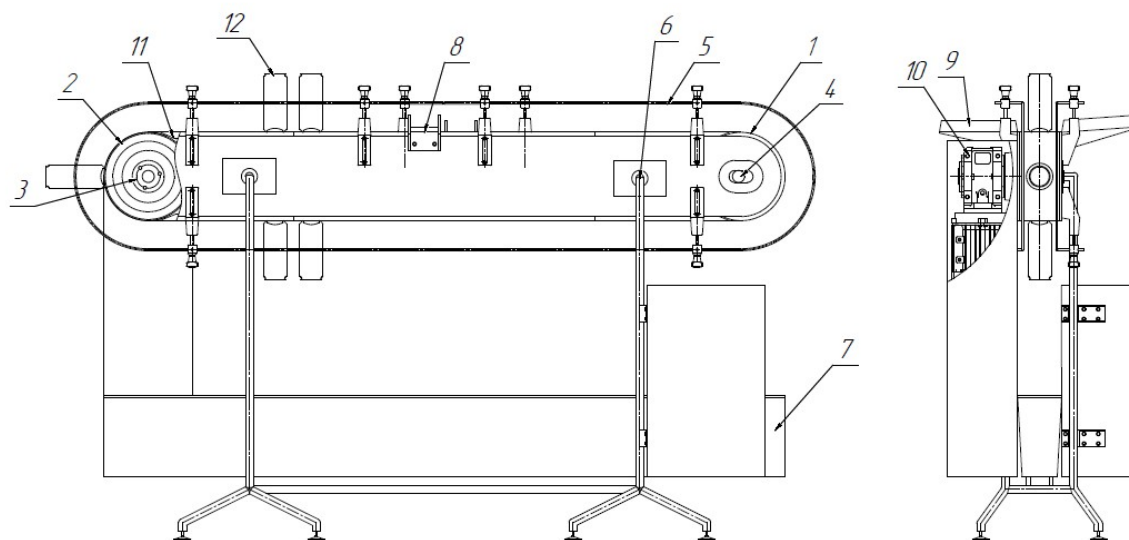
Конвеєрна система для транспортування металевої споживчої упаковки
